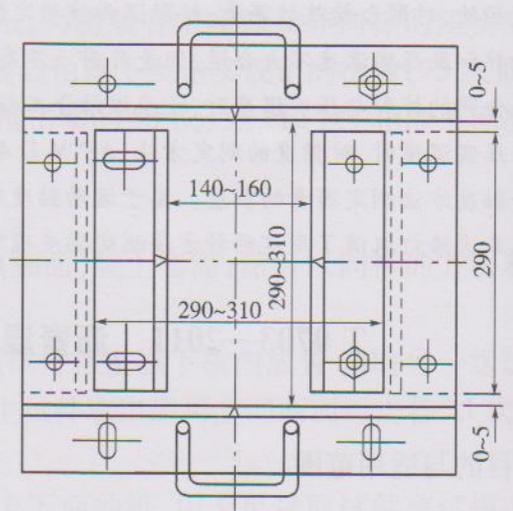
车辙试验试模 (尺寸单位: mm)
